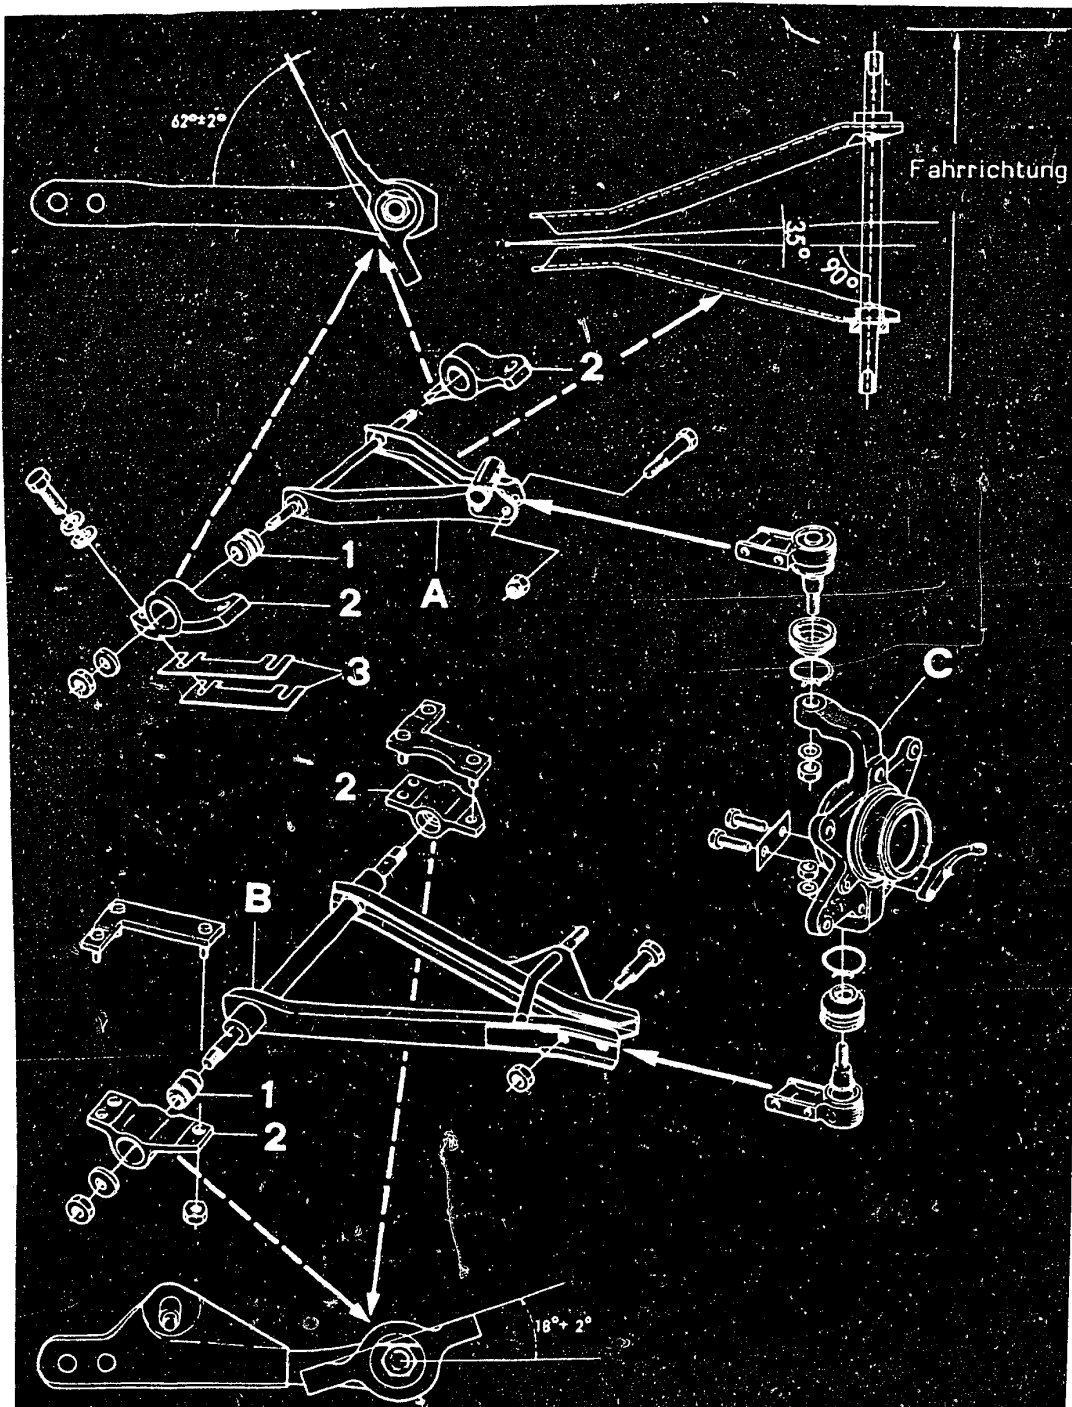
Vorderradaufhängung mit dem asymmetrischen oberen Querlenker (oben rechts): A Oberer Querlenker – B Unterer Querlenker – C Achsschenkelgehäuse – 1 Gummibuchse – 2 Lagerung – 3 Ausgleichsscheiben für Radsturz und Nachlauf.
